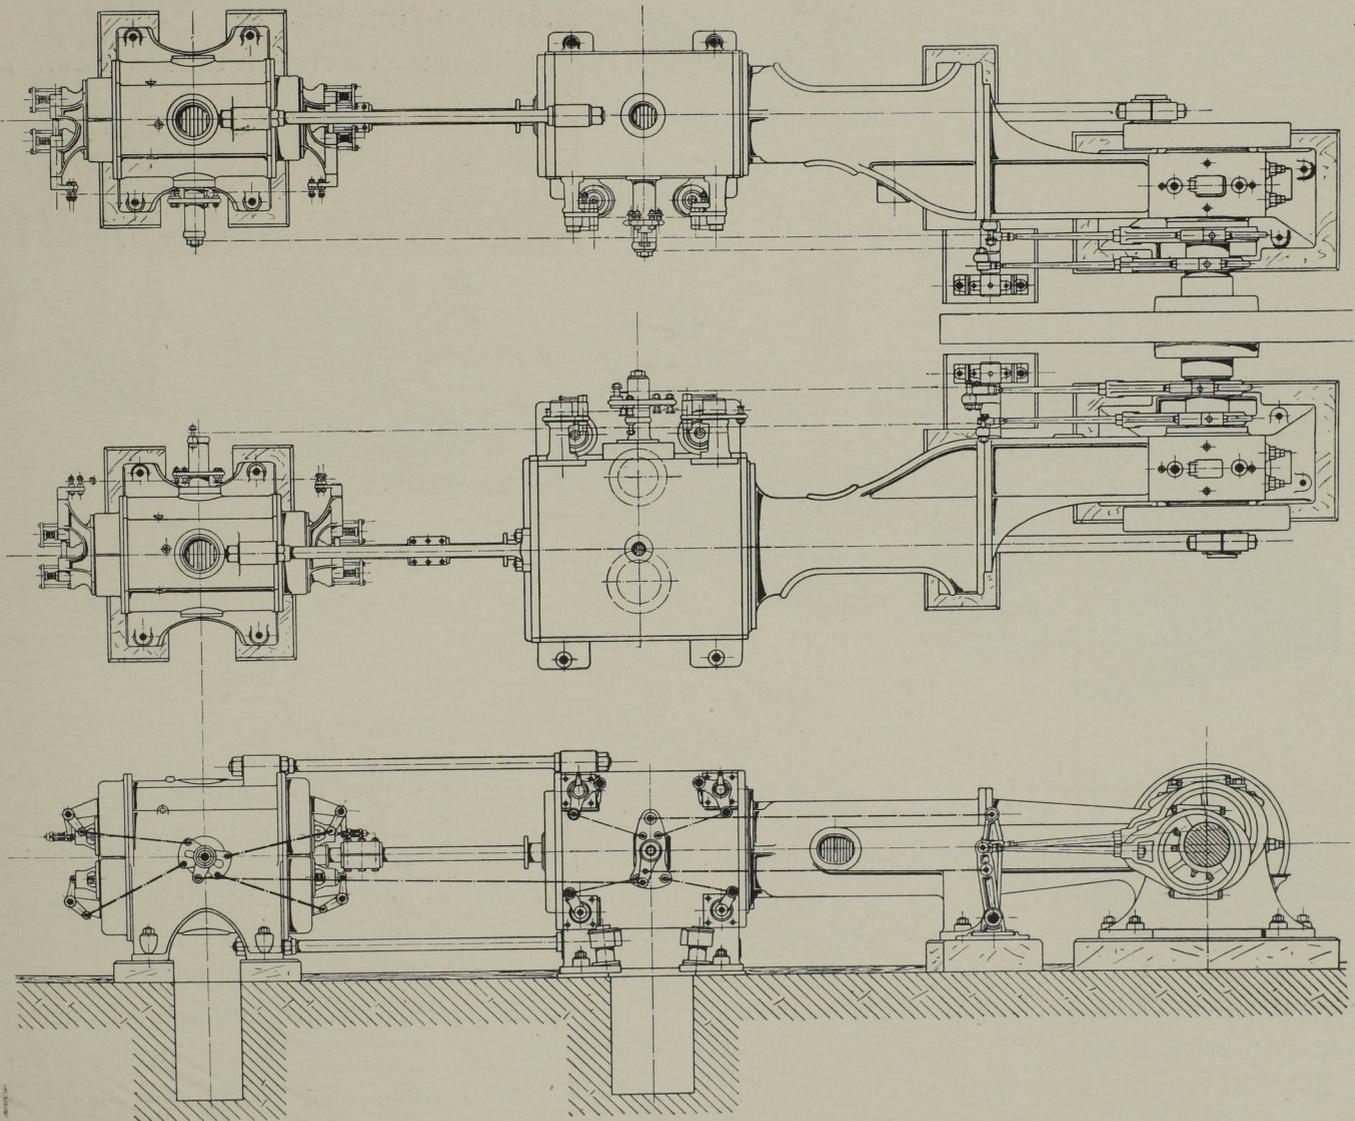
Grundriss und Seitenansicht der Maschine. Massst. 1:64.
